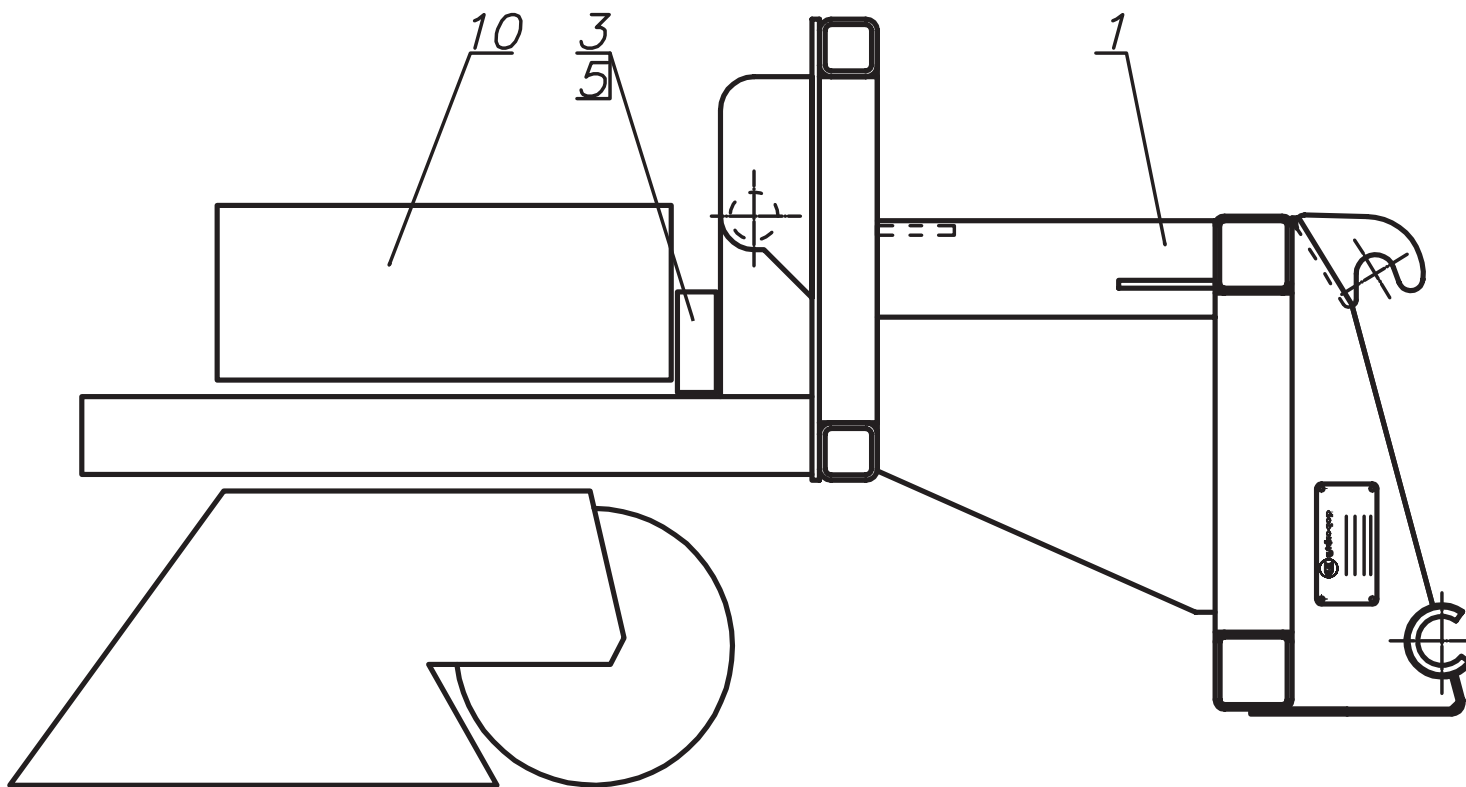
211.45.81.000	Установка подметально-уборочного оборудования "TUCHEL"
